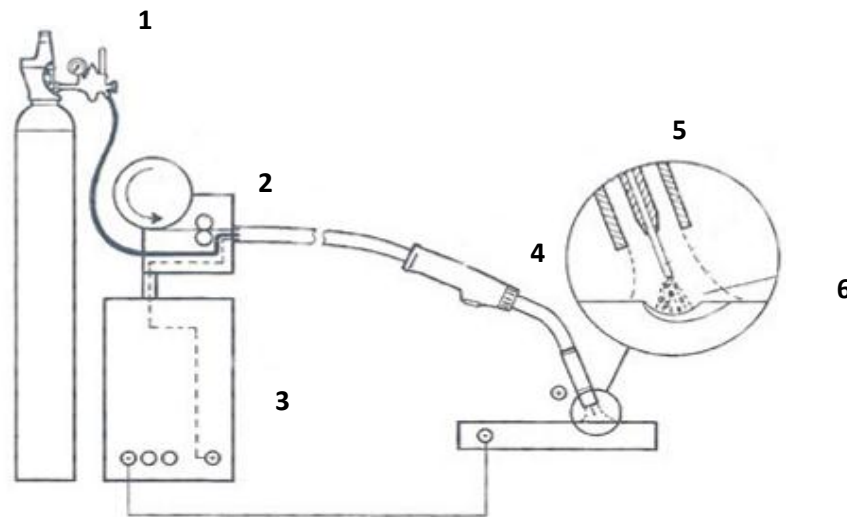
Elementos que intervienen en el proceso de soldadura MAG.
